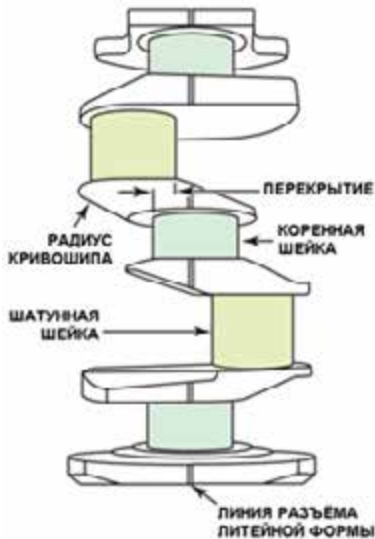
Литой коленчатый вал, показывающий частичное перекрытие шейки коренного подшипника шейкой шатунного подшипника, и прямую, узкую линию разъема литейной формы. Величина перекрытия определяет прочность коленчатого вала; источник: *Pearson Education, Inc.
